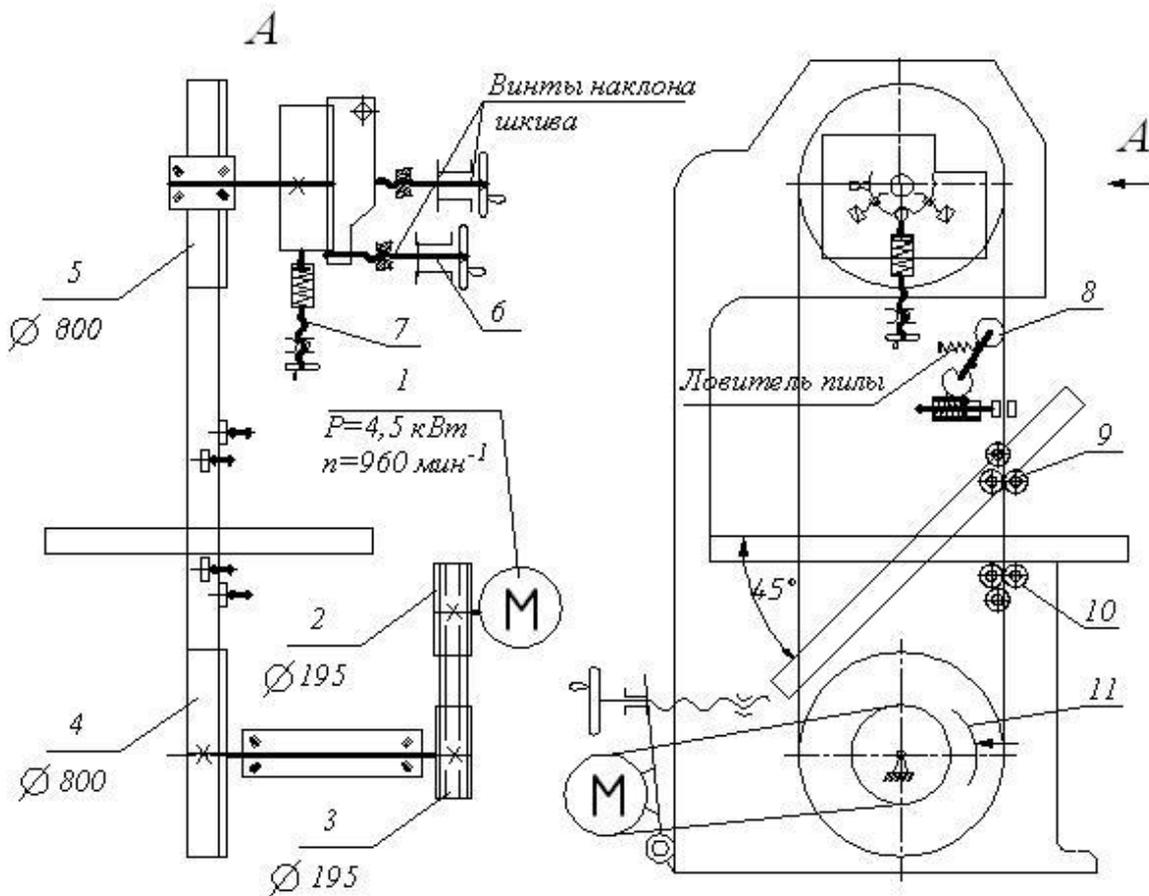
Кинематическая схема ленточнопильного станка ЛС80-5
